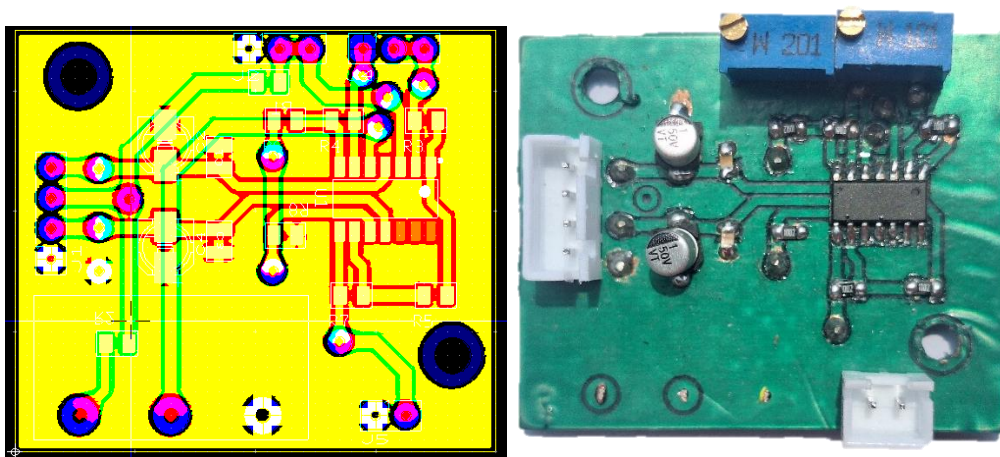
Diseño y manufacturación del PCB para acondicionar la señal del transductor PT100
